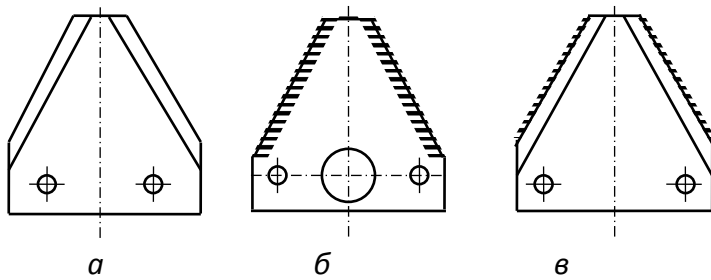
Основные варианты исполнения сегментов сегментно-пальцевого режущего аппарата: а – с гладкой режущей кромкой; б – с рифленной режущей кромкой; в – с режущей кромкой с зубуринами
